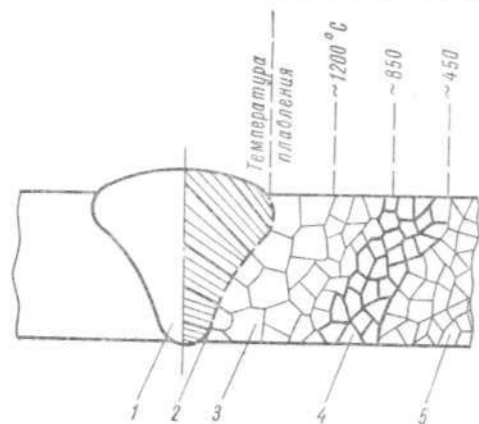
Строение околошовной зоны сварного шва аустенитной стали.
